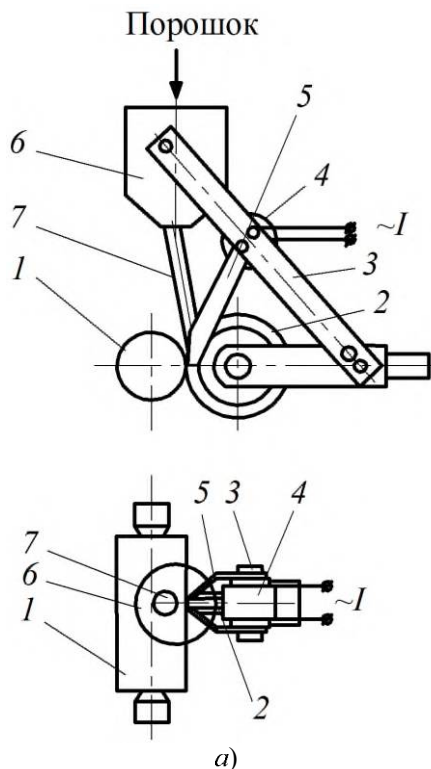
Приспособление для подачи и удержания порошка в зоне наплавки:
